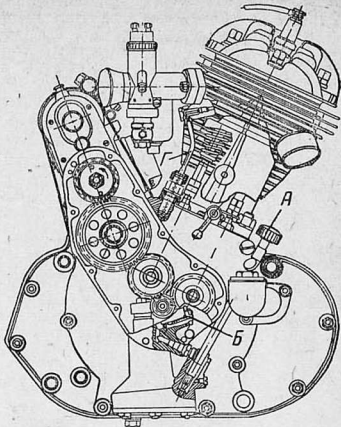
Двигатель АМ-600. А—регулирующая игла; Б—редукционный клапан; Г—трубка смазки направляющей всасывающего клапана
